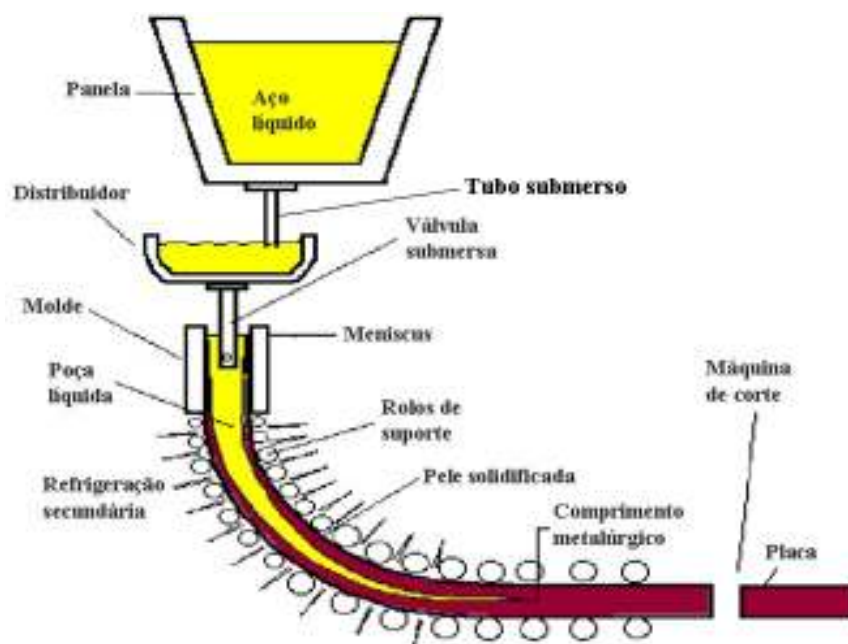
Desenho esquemático da seção transversal da máquina de lingotamento contínuo de placas. (Fonte: http://ccc.illinois.edu/images/cast_techniques_sized.jpg. Acesso em 02/04/2014).
